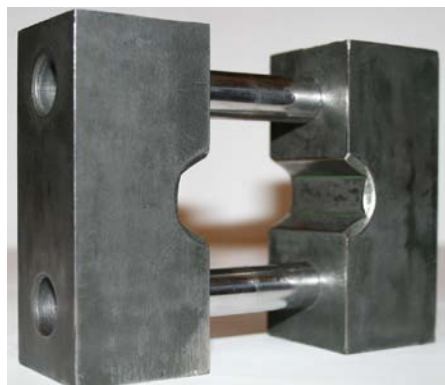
Общий вид пресс-матрицы для опрессовки оконцевателей полимерных линейных изоляторов ЛК70-35
